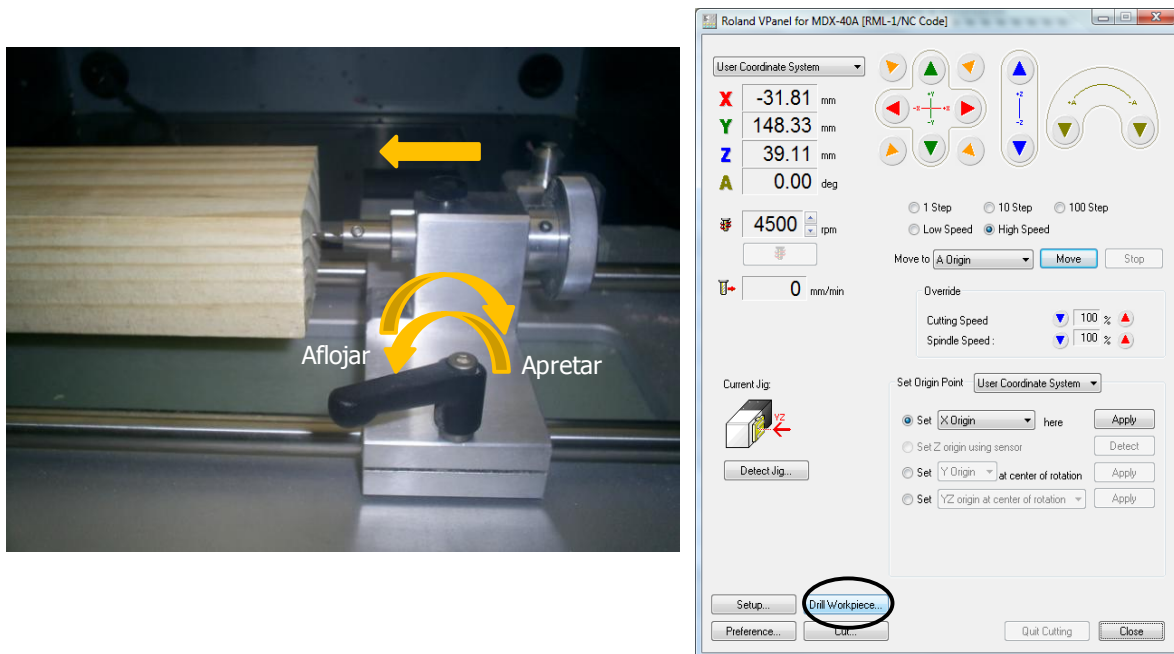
Colocar la punta del taladro contra la superficie de la pieza de trabajo y seleccionar "Drill Workpiece" en Vpanel.
